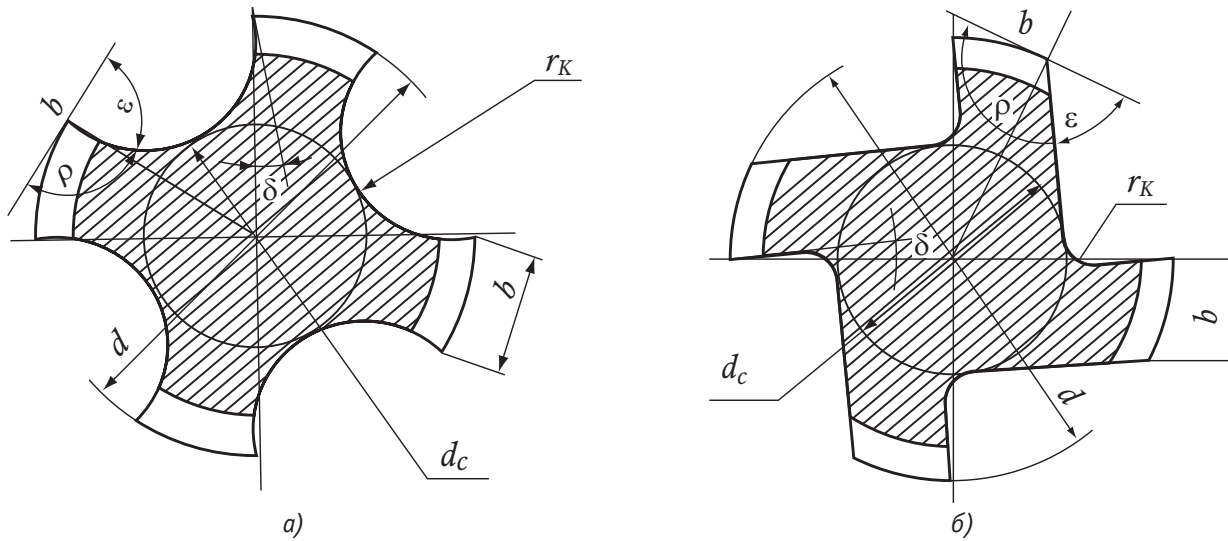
Типовые профили стружечных канавок: а – однорадиусный профиль; б – прямолинейный профиль
